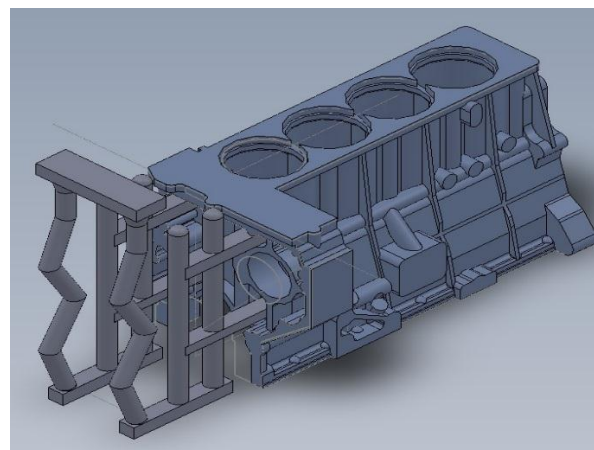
3D-модель отливки блок-картера с технологической литниково-питающей системой
